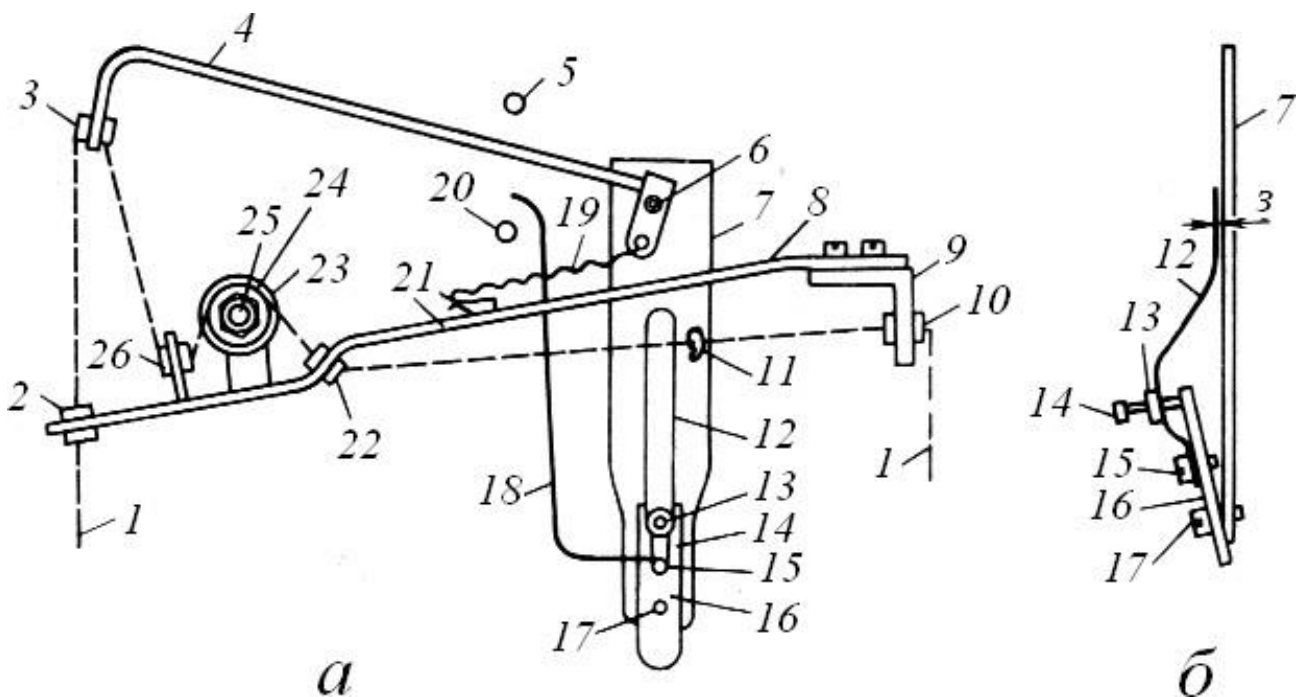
Конструктивна схема нитконатяжного пристрою.
